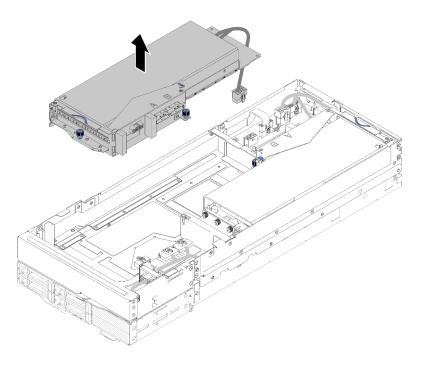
Removendo o conjunto de placa riser frontal do nó de expansão
